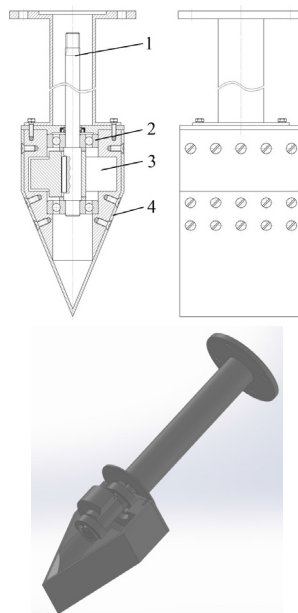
Клиновой подбойник: 1 – вал; 2 – подшипник; 3 – дебаланс; 4 – корпус.
